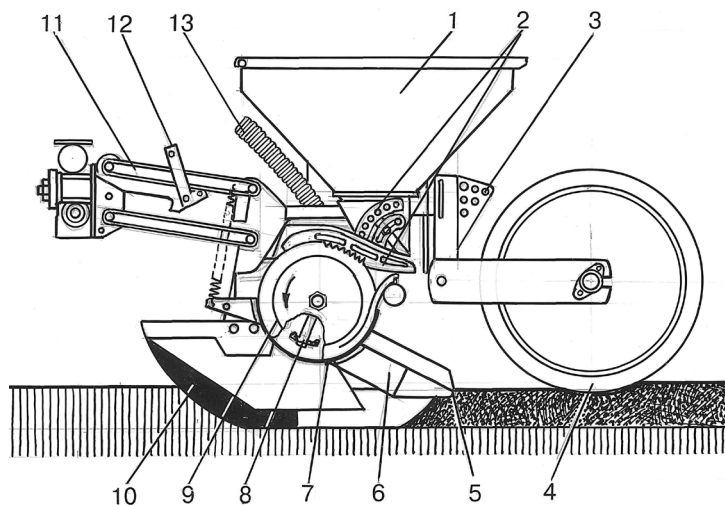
Посевная секция сеялки точного высева для заделки семян на глубину до 12 см: 1 – семенная банка; 2 – отсекаль лишних семян со шкалой; 3 – регулятор глубины; 4 – опорно-прикатывающий каток; 5 – опорняющий клапан; 6 – загортач; 7 – сбрасыватель; 8 – ролик; 9 – высеваящий аппарат; 10 – сошник; 11 – подвеска; 12 – фиксатор подвески; 13 – вакуумный шланг
